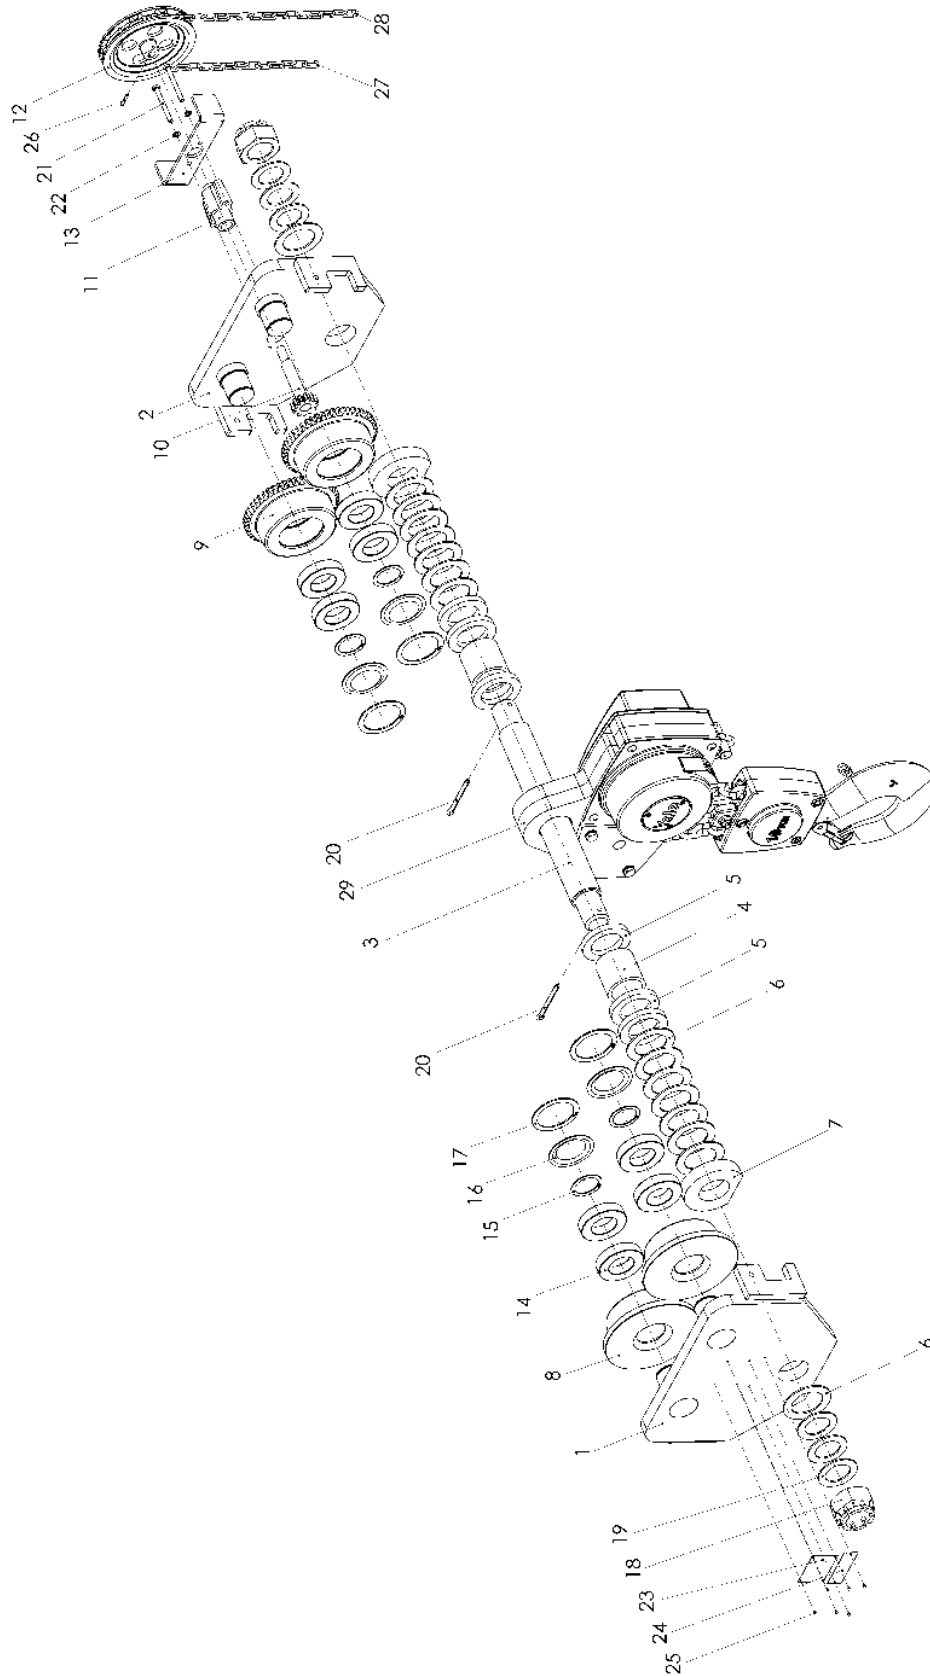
CARRO DE ENGRANAJES DE 10 TONELADAS
